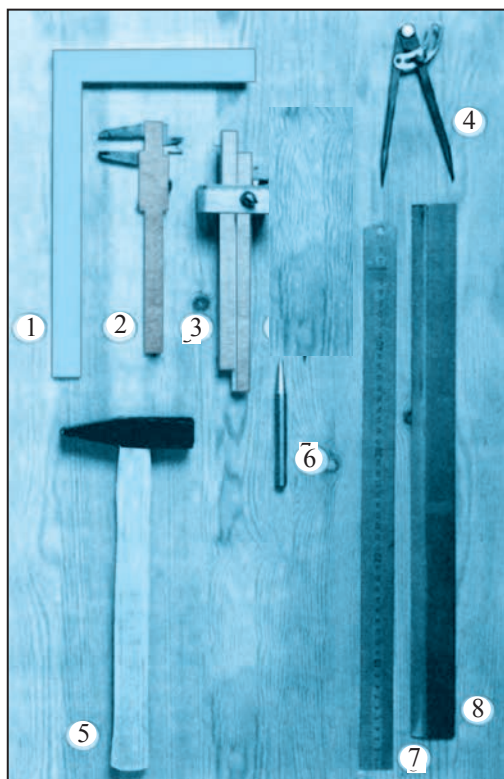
Измерительные и разметочные инструменты: 1 – 90° угольник; 2 – штангенциркуль; 3 – масштабная линейка; 4 – разметочный циркуль; 5 – слесарный молоток; 6 – кернер; 7–8 – линейки.
